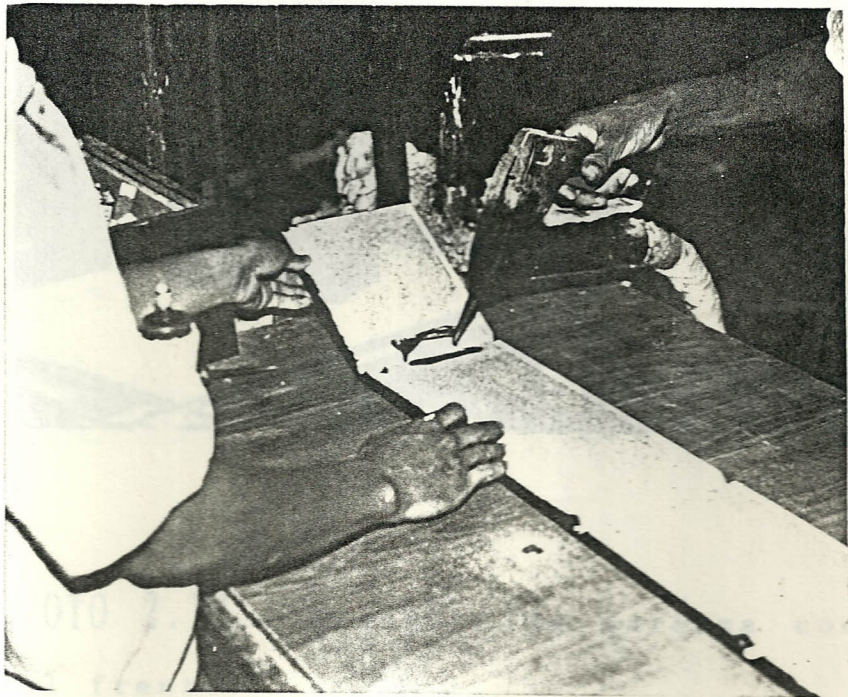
Ensamble de gabinete principal o carcasa.
